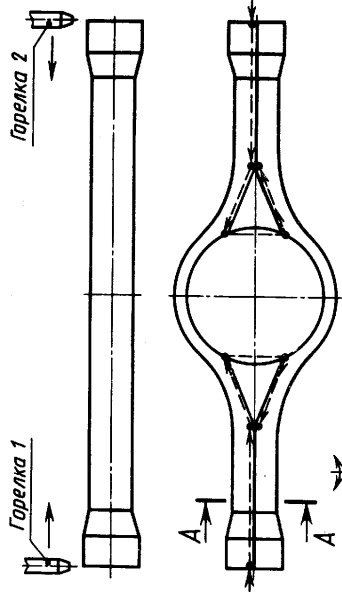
Сварка продольных швов корпуса картера (второй проход)
